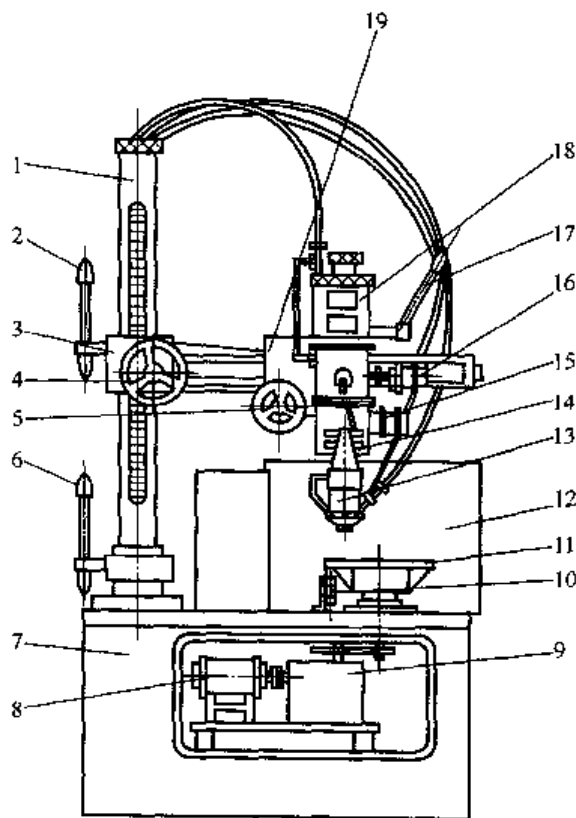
DP-300 型等离子弧堆焊设备的机械结构示意图
